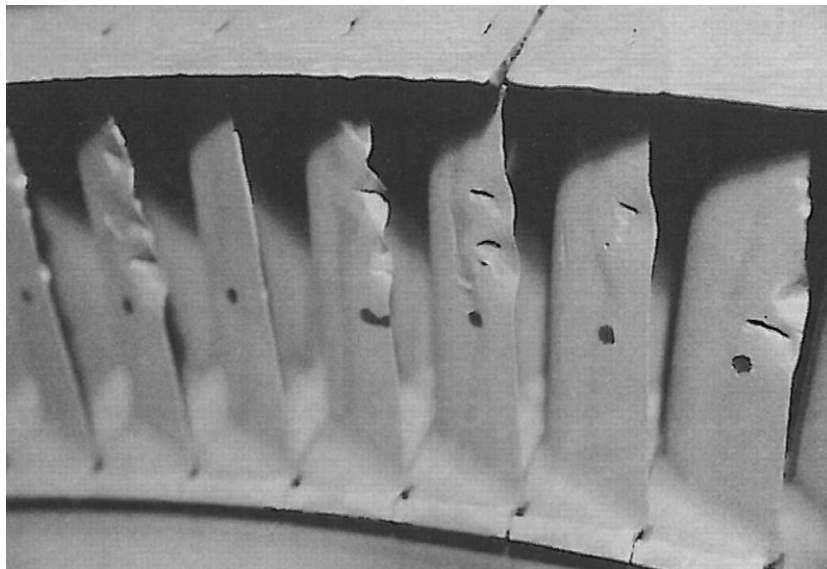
Cráteres de impacto sobre el borde de ataque de álabes del rotor
